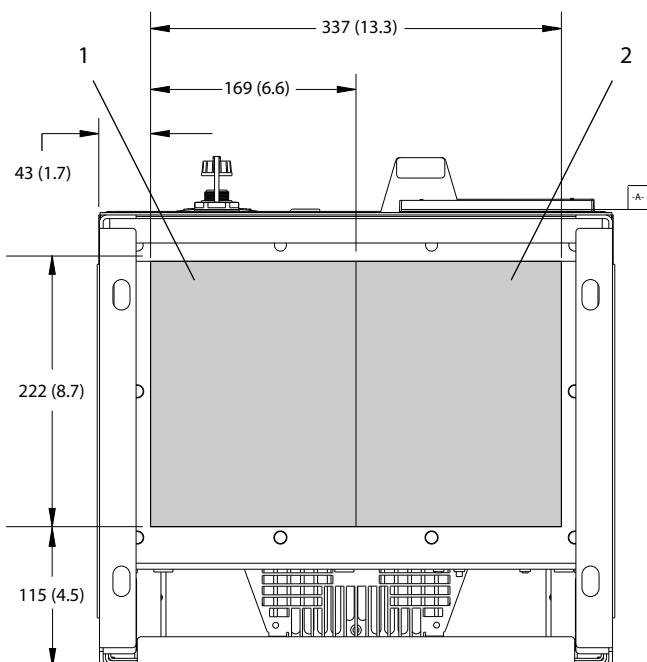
Dimensi Akses Heat Sink untuk D8h
